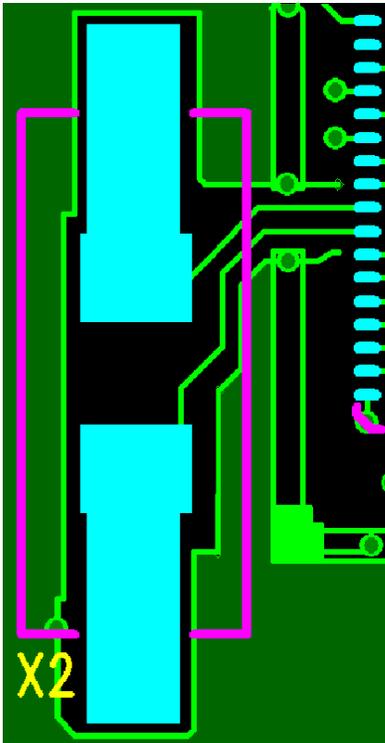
PCB トップ・メタル層の水晶発振器信号からのシールド
